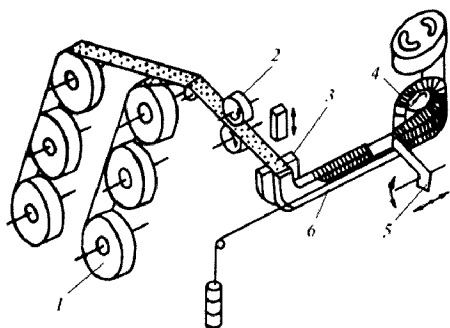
Схема установки механизированной сборки лепестковых кругов:
